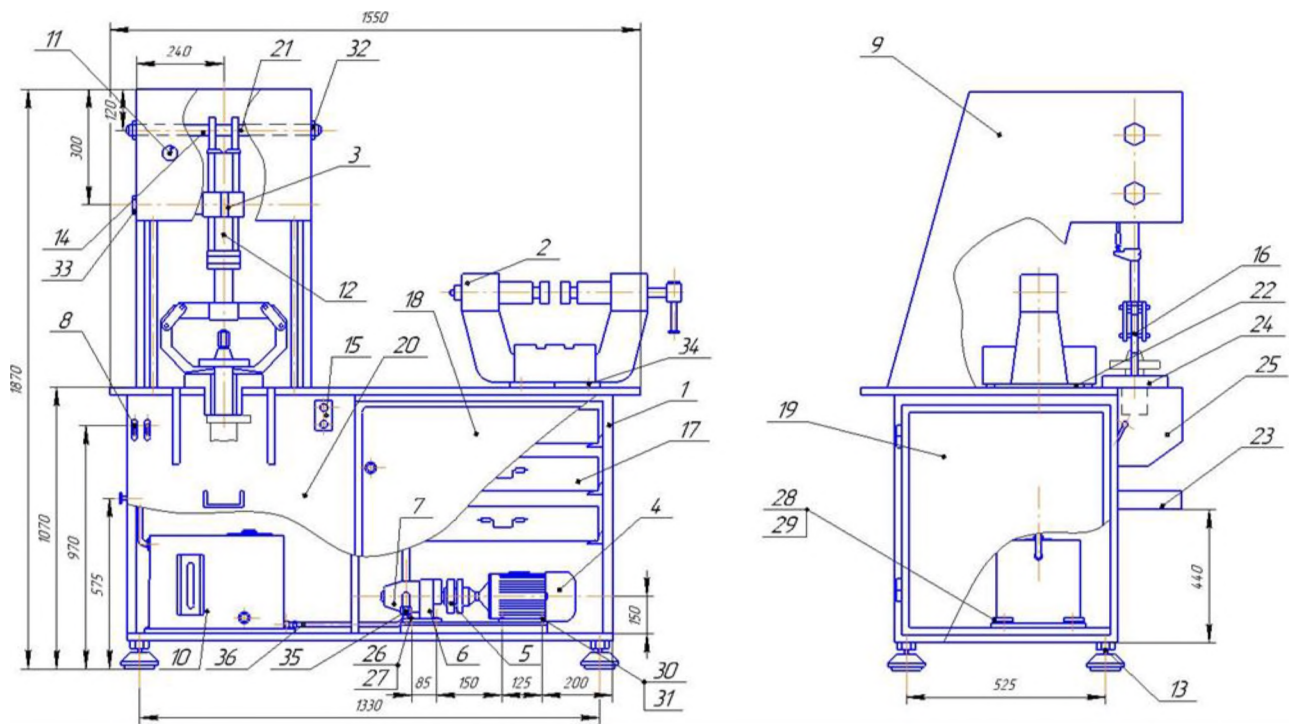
Загальний вид конструкції станда: 1 – Рама; 2 – Струбцина; 3 – Опора фіксуюча; 4 – Електродвигун; 5 – Муфта; 6 – Пристрій для кріплення; 7 – Гідравлічний насос; 8 – Гідророзподільник; 9 – Укосина; 10 – Бак гідравлічний; 11 – Манометр; 12 – Гідроциліндр; 13 – Опора; 14 – Панель кронштейна; 15 – Кнопочка станція; 16 – Знімач; 17 – Ящик; 18 – Двері передні; 19 – Двері бічні; 20 – Панель ліва; 21 – Вісь; 22 – Плита опорна; 23 – Уловлювач; 24 – Втулка упорна; 25 – Ребро; 26-34 – Різьбові з'єднання; 35 – З'єднання роз'ємні рукавів; 36 – Рукав
